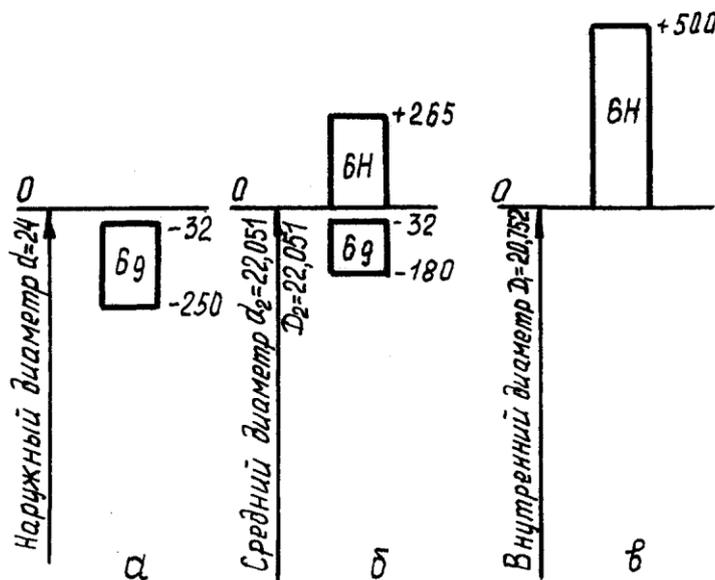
Поля допусков для диаметров резьбы M 24 – 6H/6g
